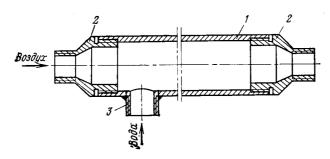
Аэратор упрощенной конструкции: 1 -кожух смесителя; 2 -переводник; 3 -втулка
